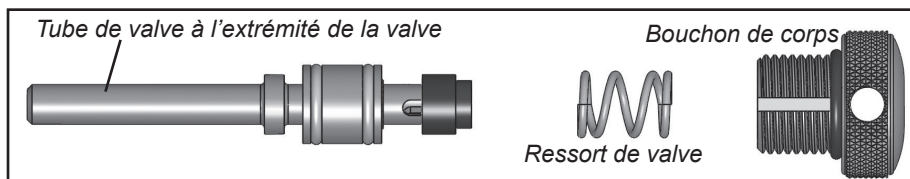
Assemblage de la valve, ressort et bouchon de corps
